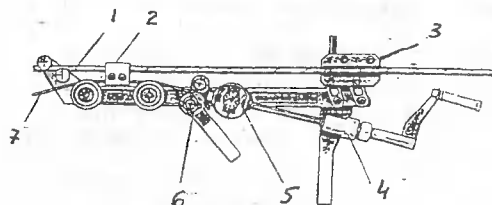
Устройство для натяжения рессорного троса:
